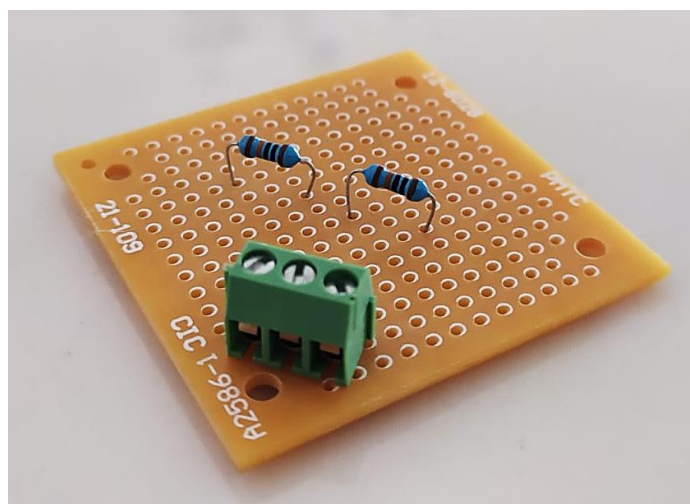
Celda de prueba para validación de dispositivo de read out
